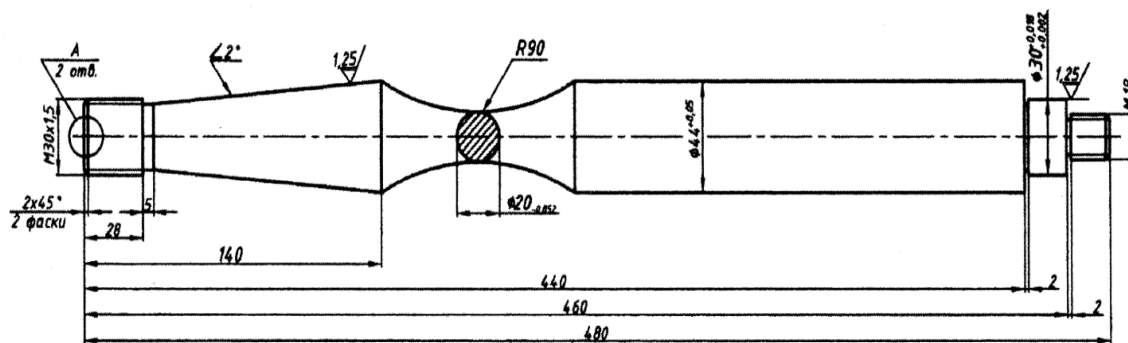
Образец-модель для испытаний на консольный изгиб с кручением
